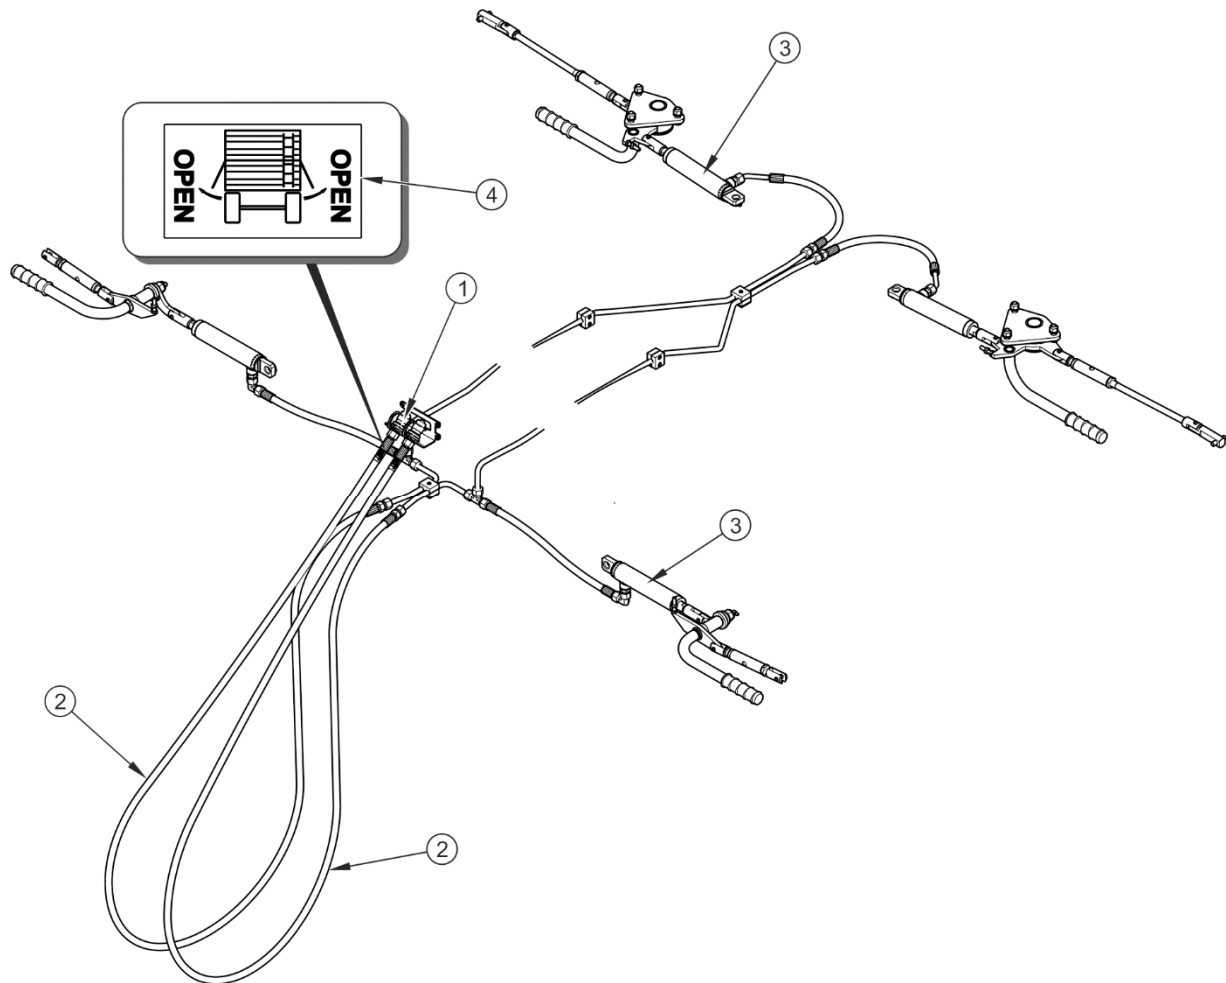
Construction du circuit hydraulique de déverrouillage des ridelles
